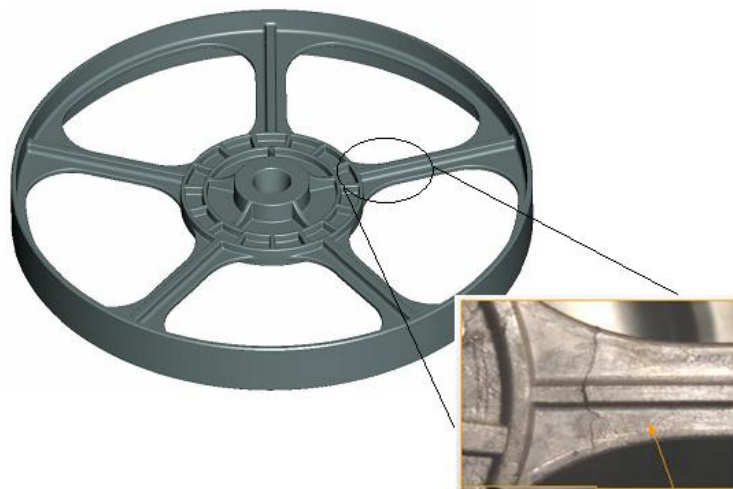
Fractura en uno de los brazos de la polea agitador de aluminio.
